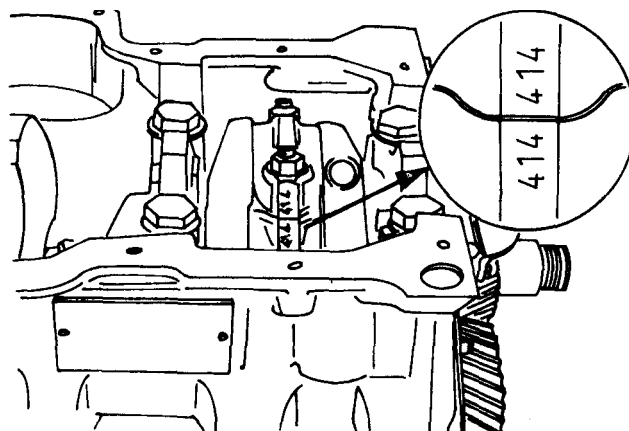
Обозначения на шатуне и крышке должны при сборке располагаться друг против друга.
